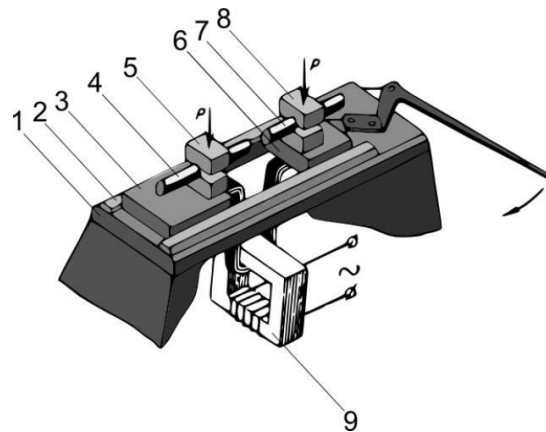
Схема машины для стыковой контактной сварки:
